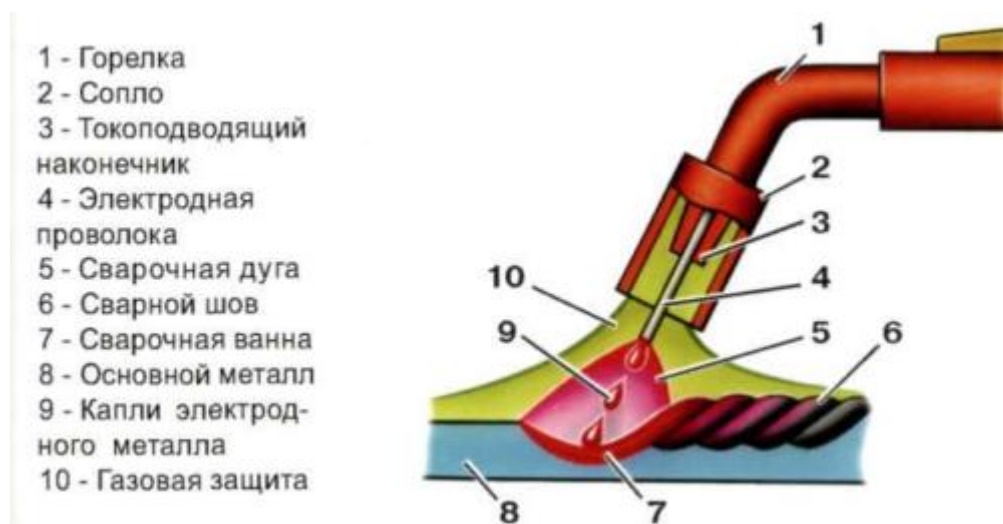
Эскиз механизированной сварки плавящимся электродом в защитных газах
